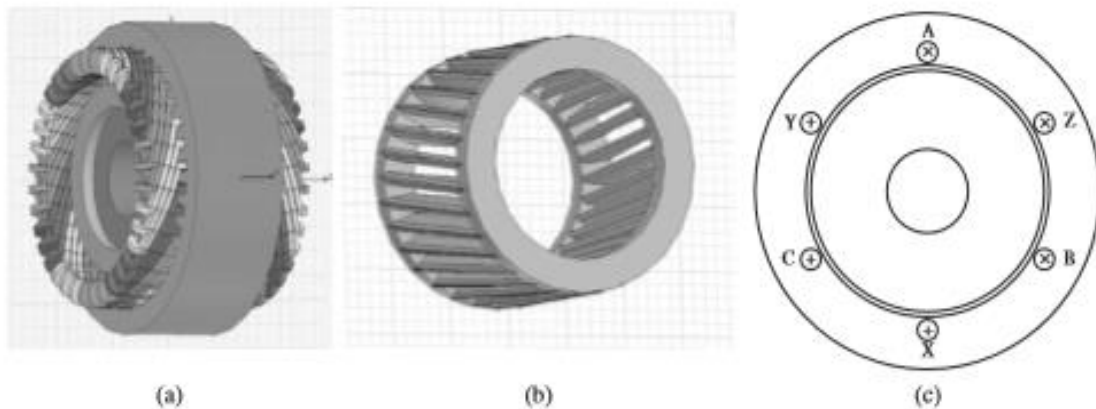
Motor de inducción: (a) rotor y estator, (b) rotor, y (c) estator
